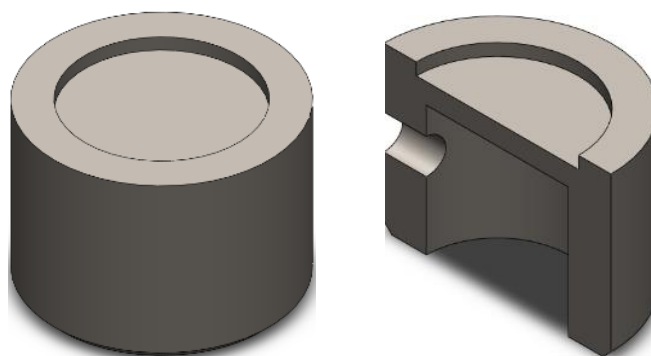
Corpo de prova (perspectiva isométrica e isométrica com corte transversal). Fonte: Autor.
